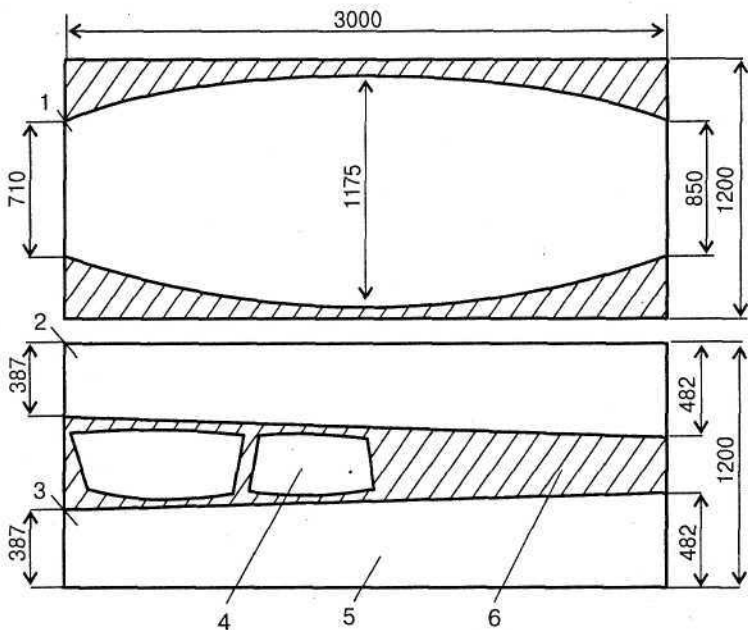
Схема раскроя листов обшивки: 1 — днище; 2, 5 — обшивка бортов; 3 — обшивка транца; 4 — обшивка носа; 6 — остаток фанеры для книц, косынок, накладок
